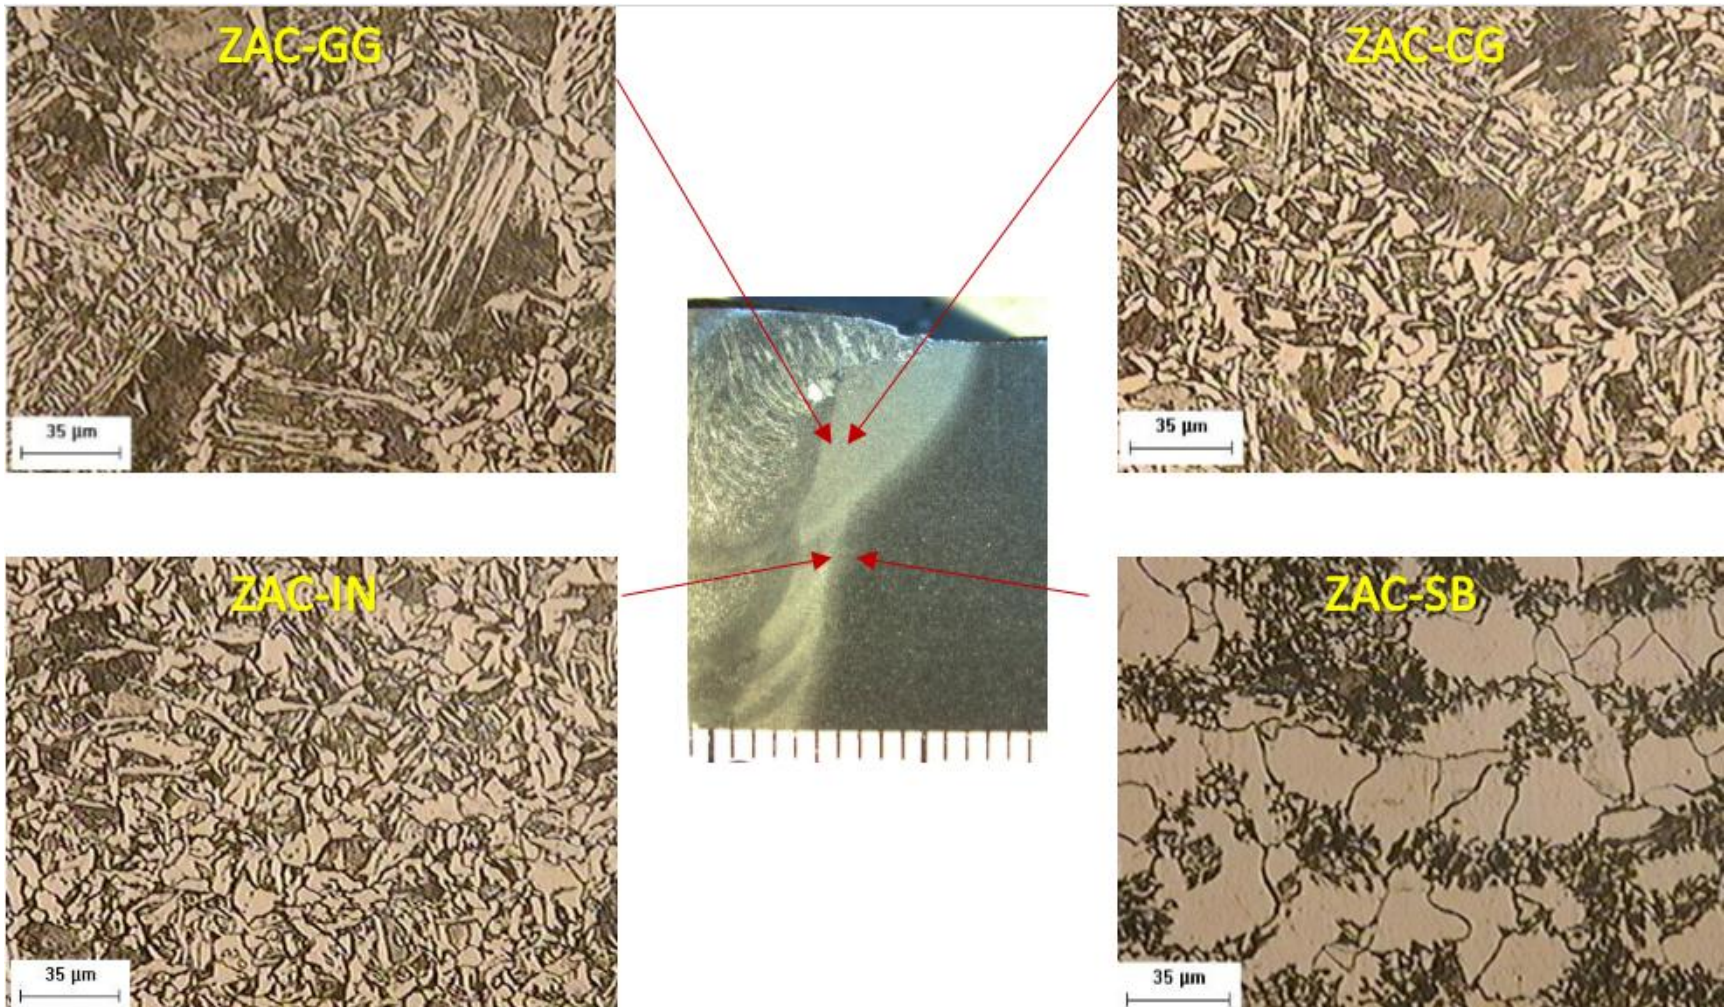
Regiones en la ZAC. Proceso de soldadura GMAW, H.I. = 2.9 KJ/mm.
